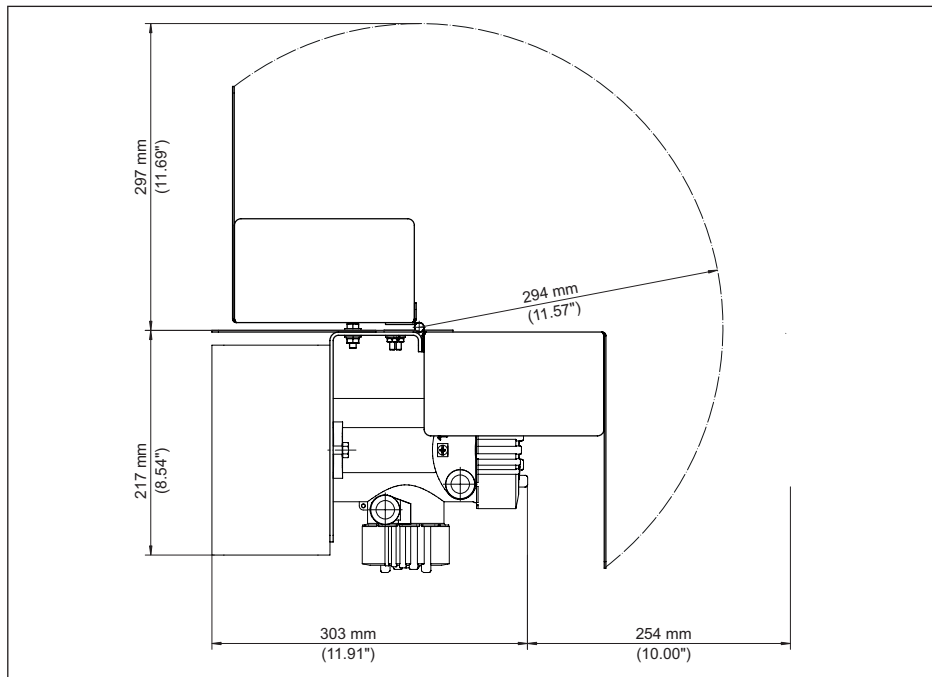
Protezione solare passiva con sensore montato orizzontalmente (area di apertura e servizio)
